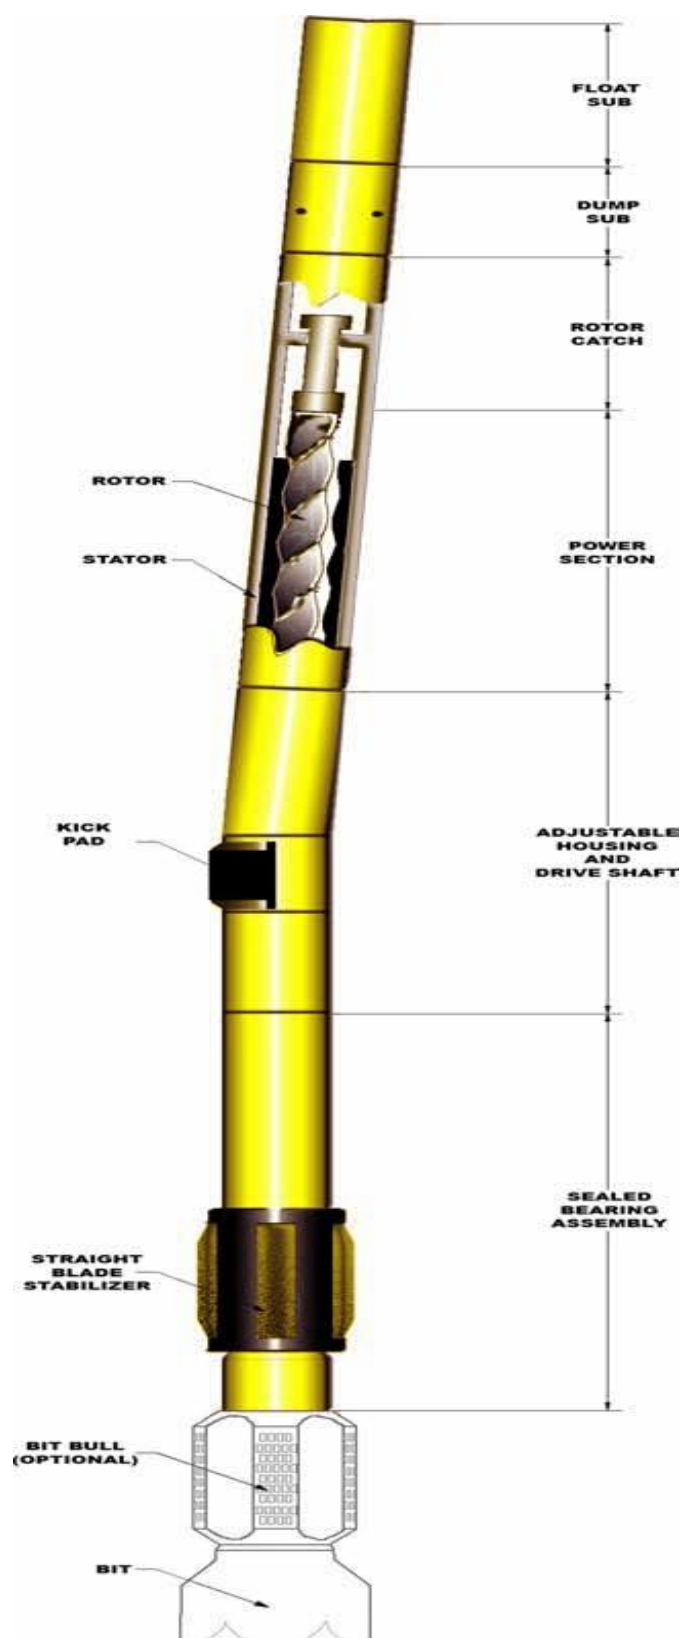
construção de trajetória, fonte- *Cougar drilling solution
